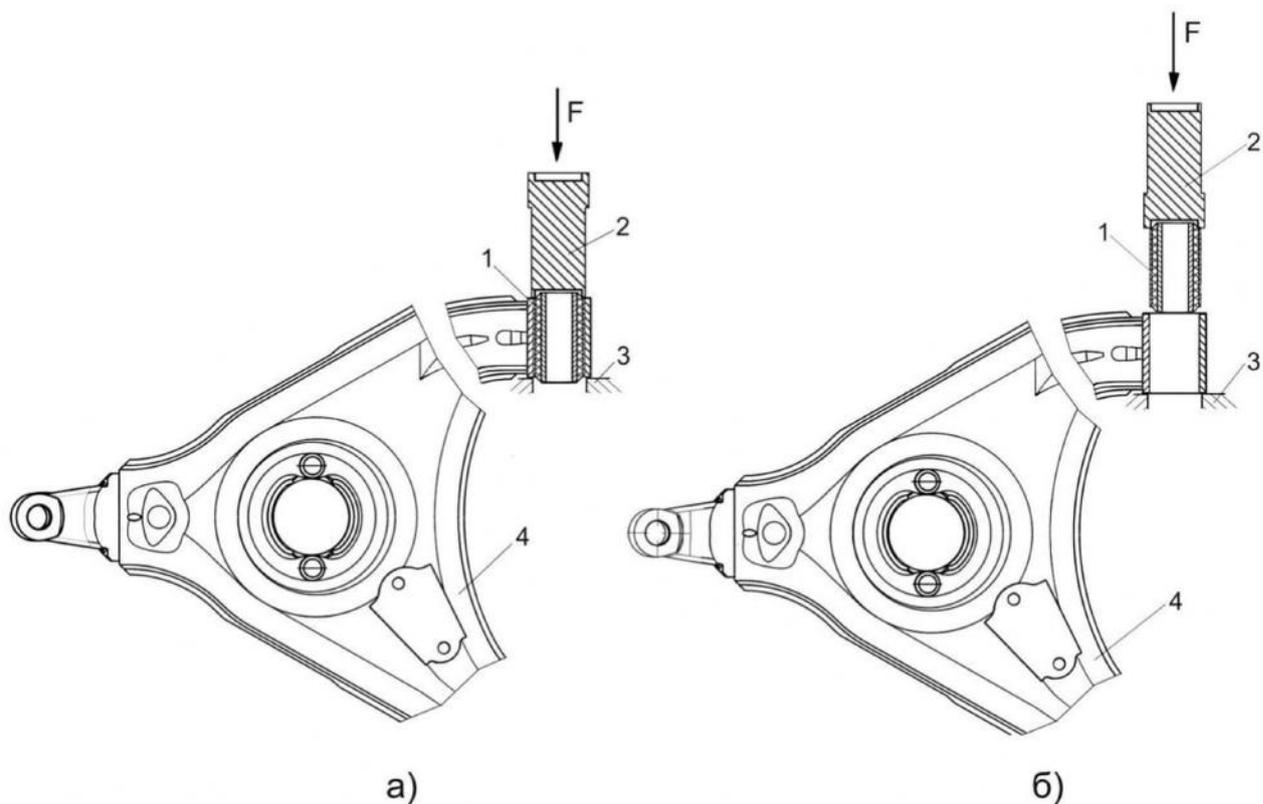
Выпрессовка и запрессовка сайлентблока нижнего рычага подвески: а - выпрессовка сайлентблока; б- запрессовка сайлентблока; 1 – сайлентблок; 2 – оправка; 3 - опора; 4 – нижний рычаг подвески
